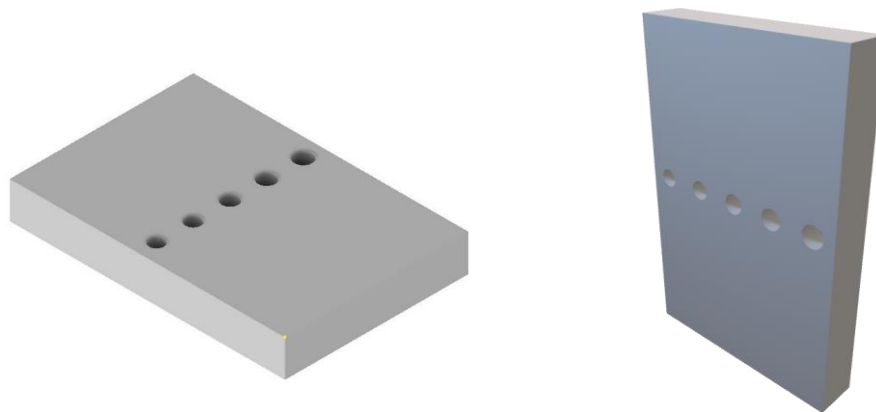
Τρισδιάστατη απεικόνιση αποστολής 39
